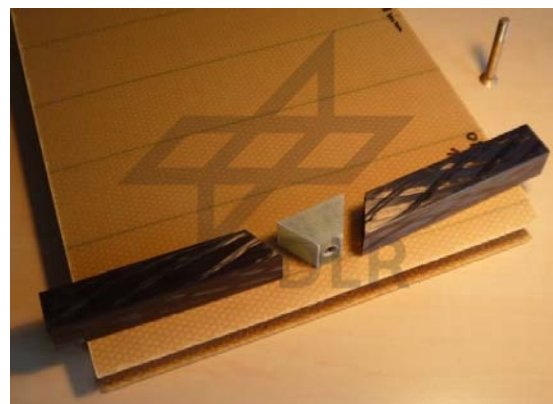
Prototyp des GFK-Trapezkörperkonzepts inkl. Mittenbohrung mit Gewindeverstärkungseinsatz zur Aufnahme der Anschlusschraube.
